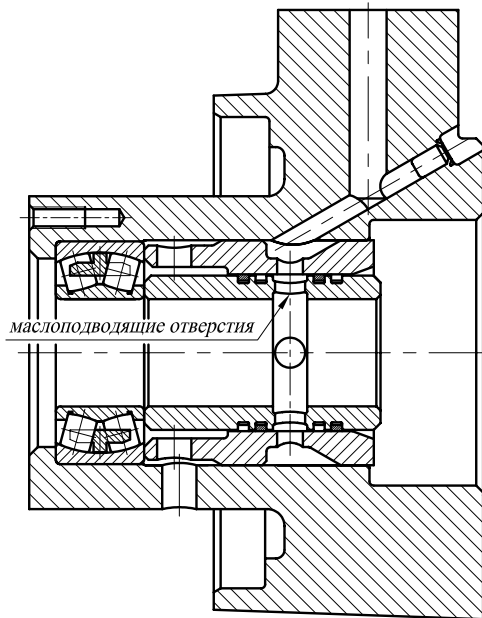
Установка распорных втулок в корпус привода вентилятора
